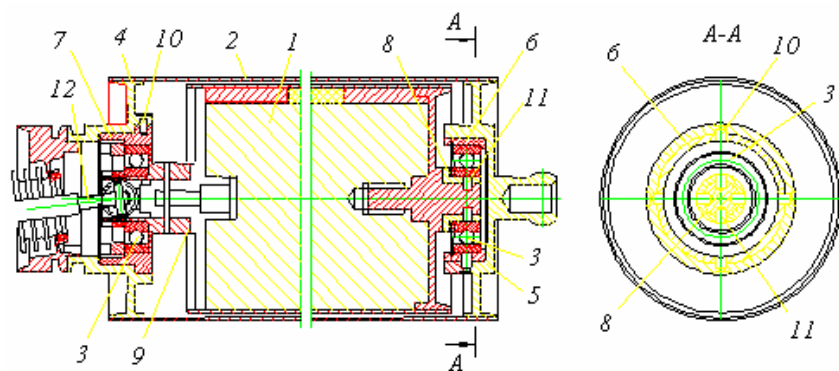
Барабан в корпусе: 1 – барабан; 2 – корпус; 3 – подшипник; 4, 5 – крышка; 6, 7 – втулка наружная; 8, 9 – втулка внутренняя; 10, 11 – шрифт радиальный; 12 – карданный вал
